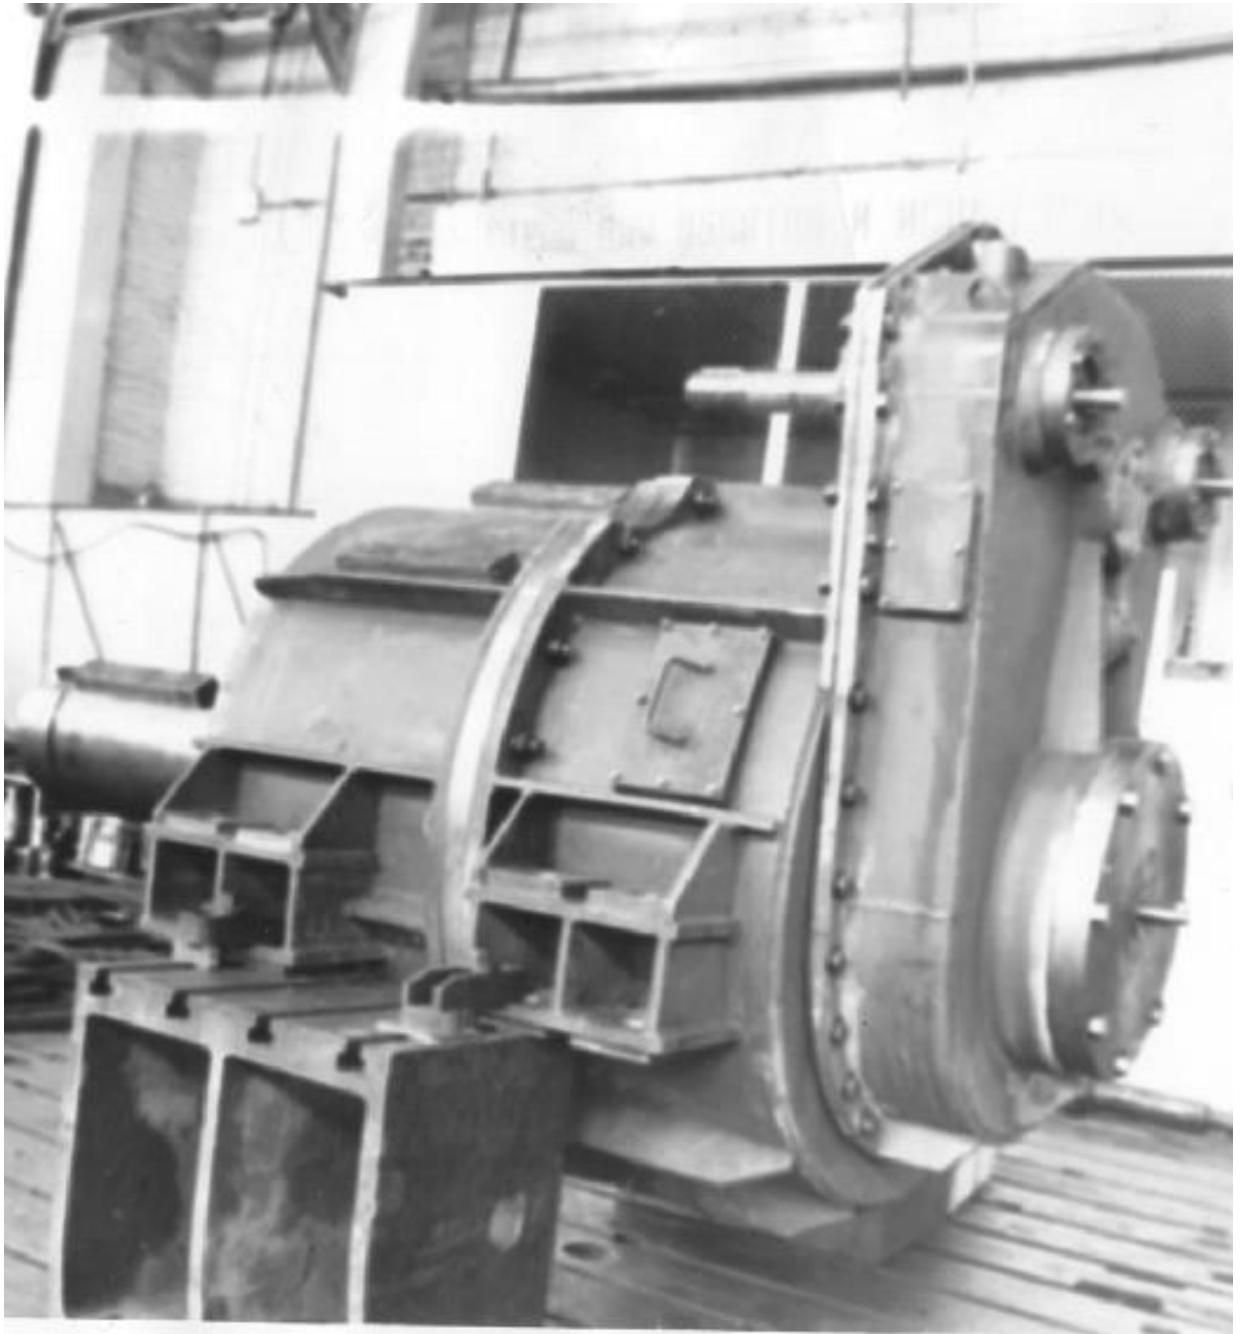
Хвильовий зубчастий редуктор В3-1120 привода повороту пересувного міксеру МП – 600АС вантажопідйомністю 600 т розплавленого металу
